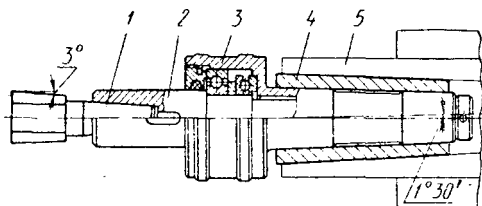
Приспособление для обработки отверстий квадратного и шестигранного профиля на токарных станках
